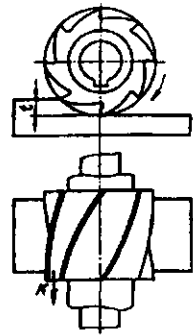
Схема фрезерования плоской поверхности цилиндрической фрезой: K — осевая составляющая силы резания; t — глубина резания
